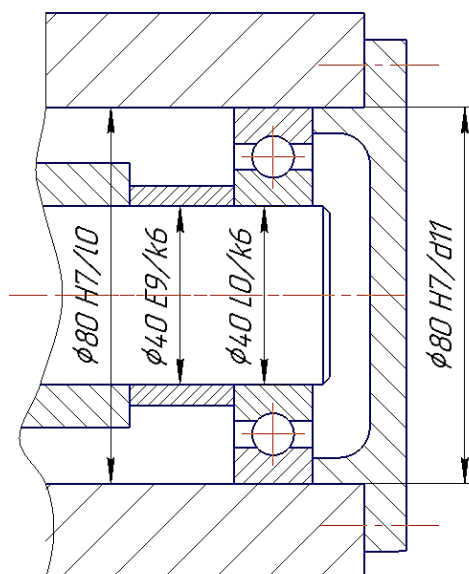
Обозначение посадок подшипников качения на чертежах
